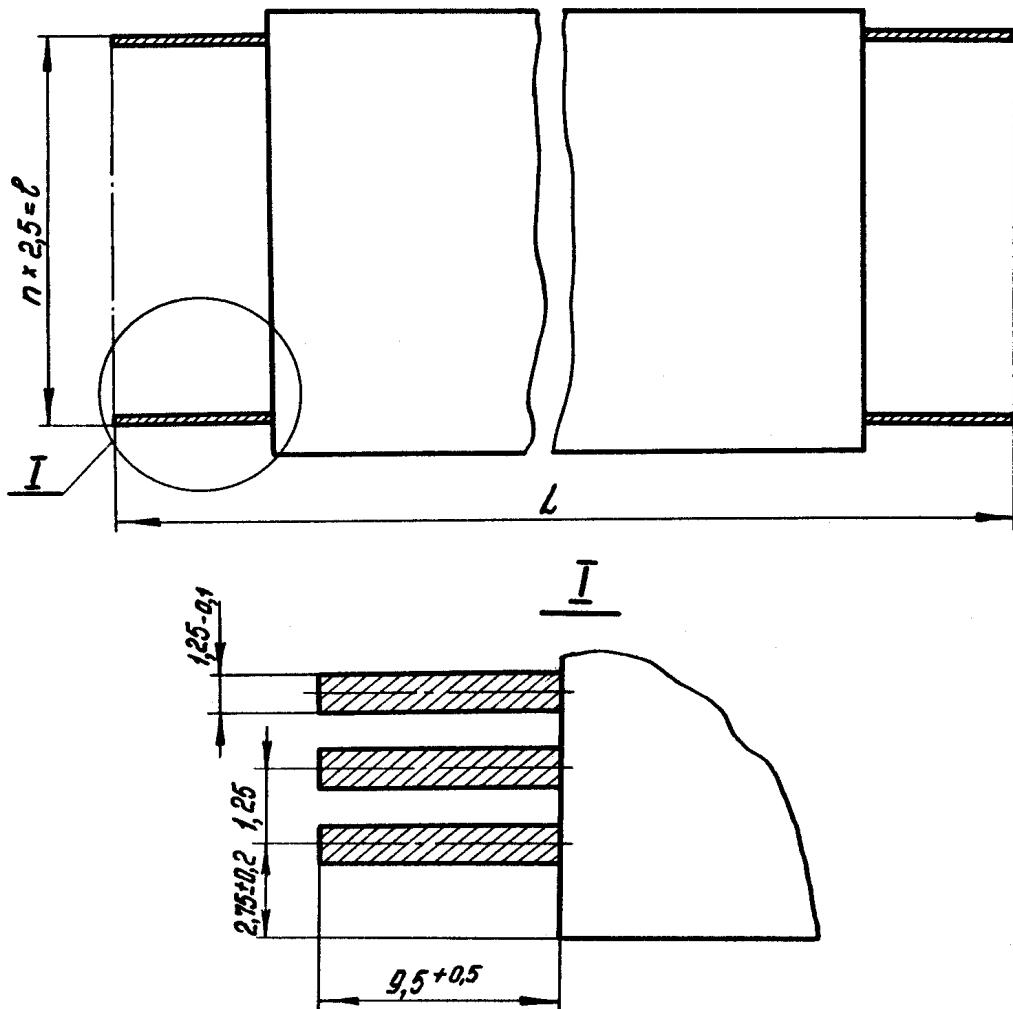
Гибкий печатный кабель с однорядными контактными лепестками одинаковой длины: L - длина кабеля (не более 348 мм); 1 - ширина кабеля (не более 57,5 мм)
